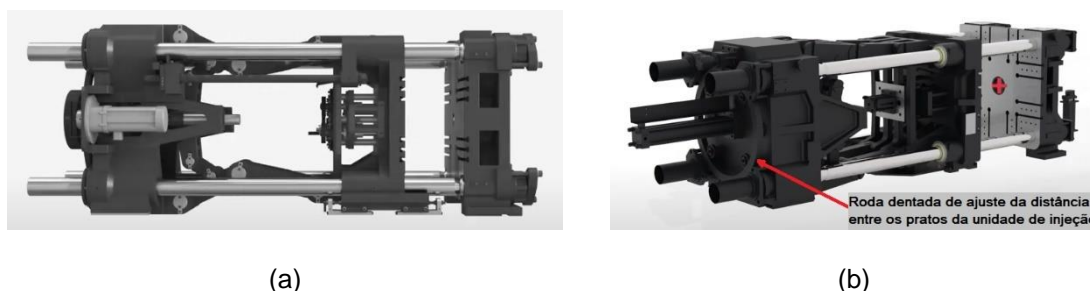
Exemplo de unidade de fecho de joalheira: (a) – joalheira que realiza o movimento do prato móvel e garante o fecho do molde; (b) – roda dentada que realiza o ajuste da espessura do molde.
